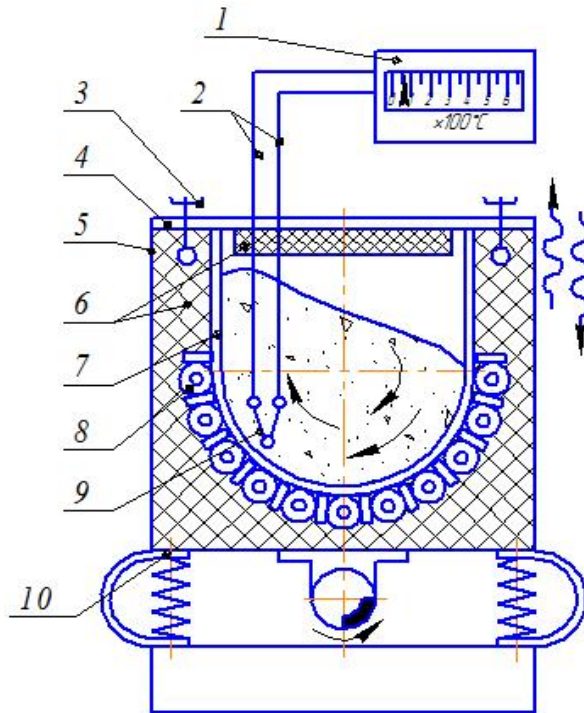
Схема пристрою для вібротермомеханічної обробки
